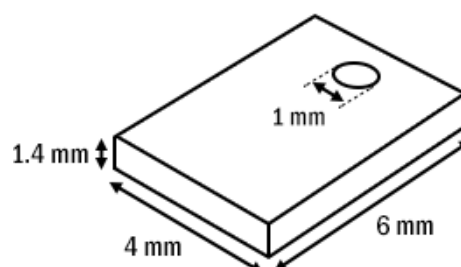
Géométrie des éprouvettes réalisées pour l'ATG du test #2
